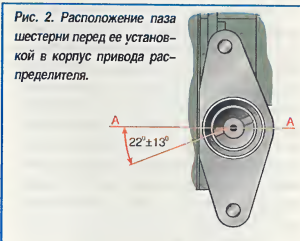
Расположение паза шестерни перед ее установкой в корпус привода распределителя.
